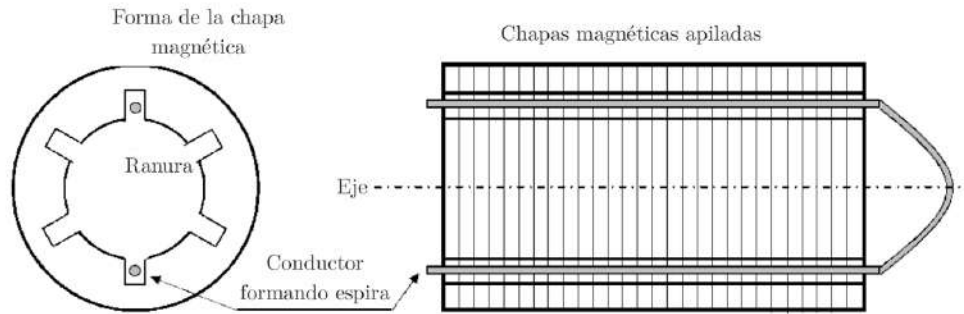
Estator de un máquina eléctrica rotatoria.
